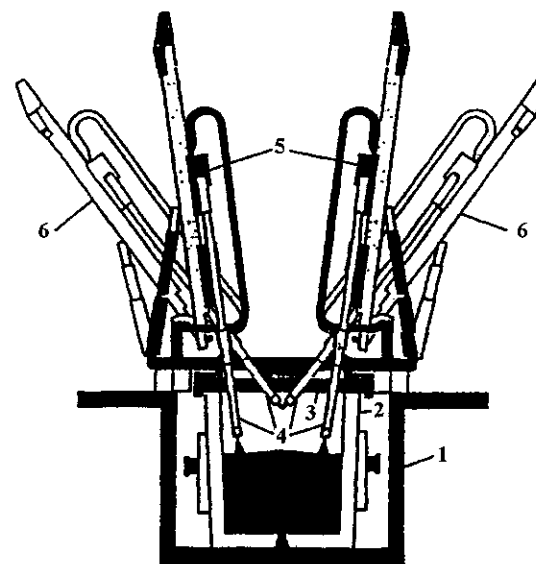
Типовая компоновка ковша-печи с плазменным нагревом:
